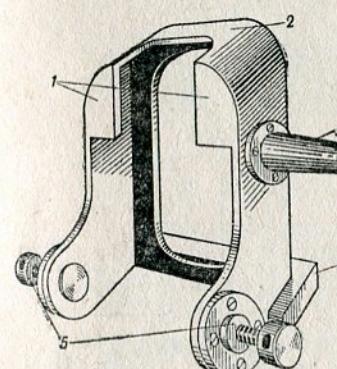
Остав для крепления фотокинопулемета на подвижных установках (вид снизу)
